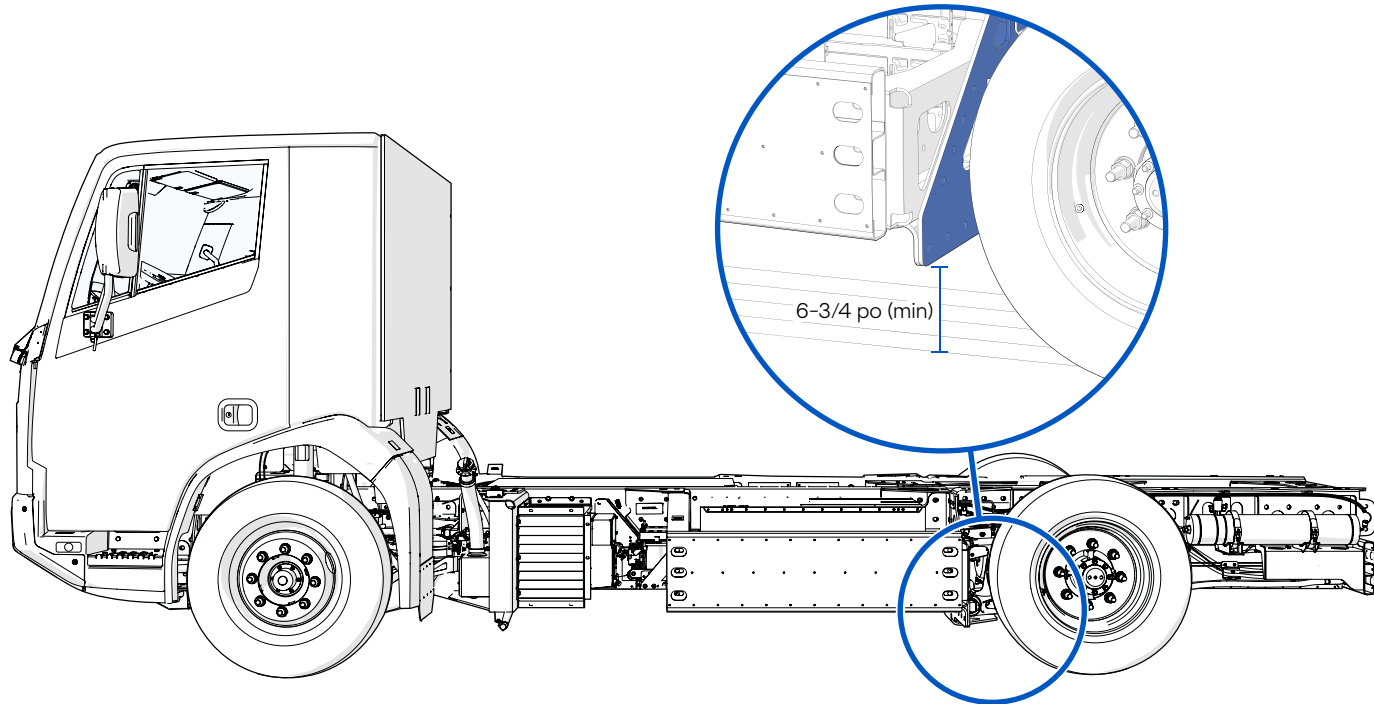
Hauteur minimum pour le remorquage par l'avant
